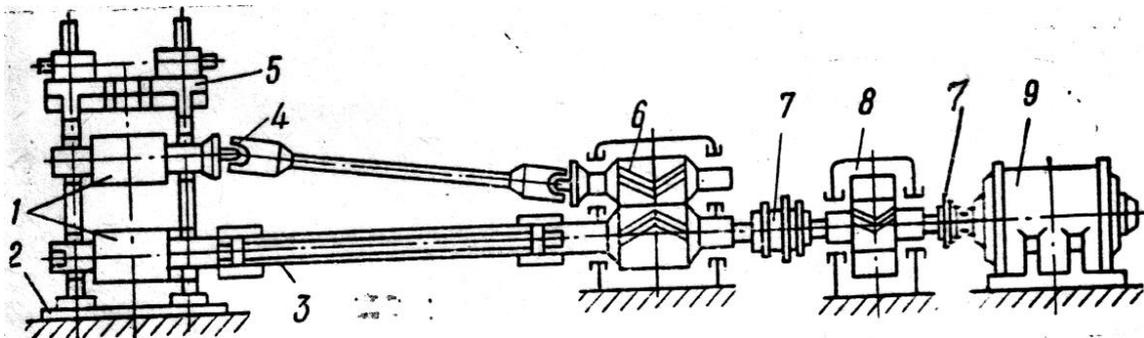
Схема головної лінії прокатного стану: 1 – валки кліті; 2 – плитовина; 3,4 – шпинделі; 5 – кліть; 6 – шестерінчаста кліть; 7 – муфта; 8 – редуктор; 9 – електродвигун.
